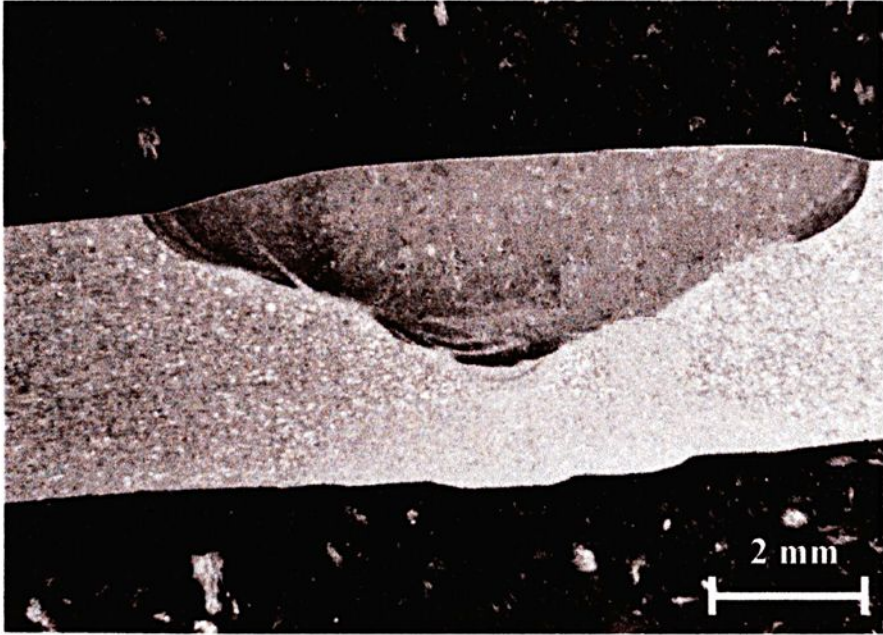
Cordão de solda para condição L2, com destaque da região da ZF.
